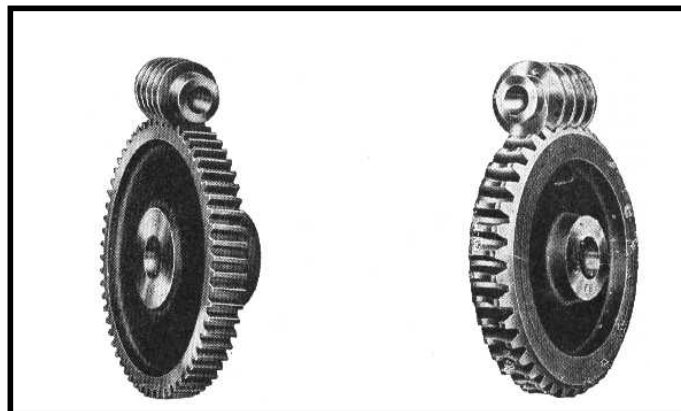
ENGRANAJES DE TORNILLO SIN FIN
